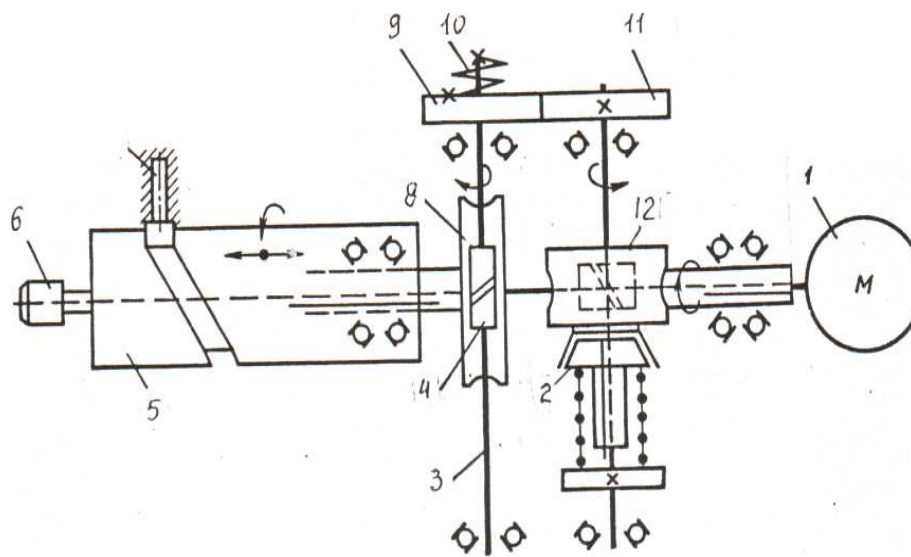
Схеми кулачкового механізму для дискретної подачі привода
